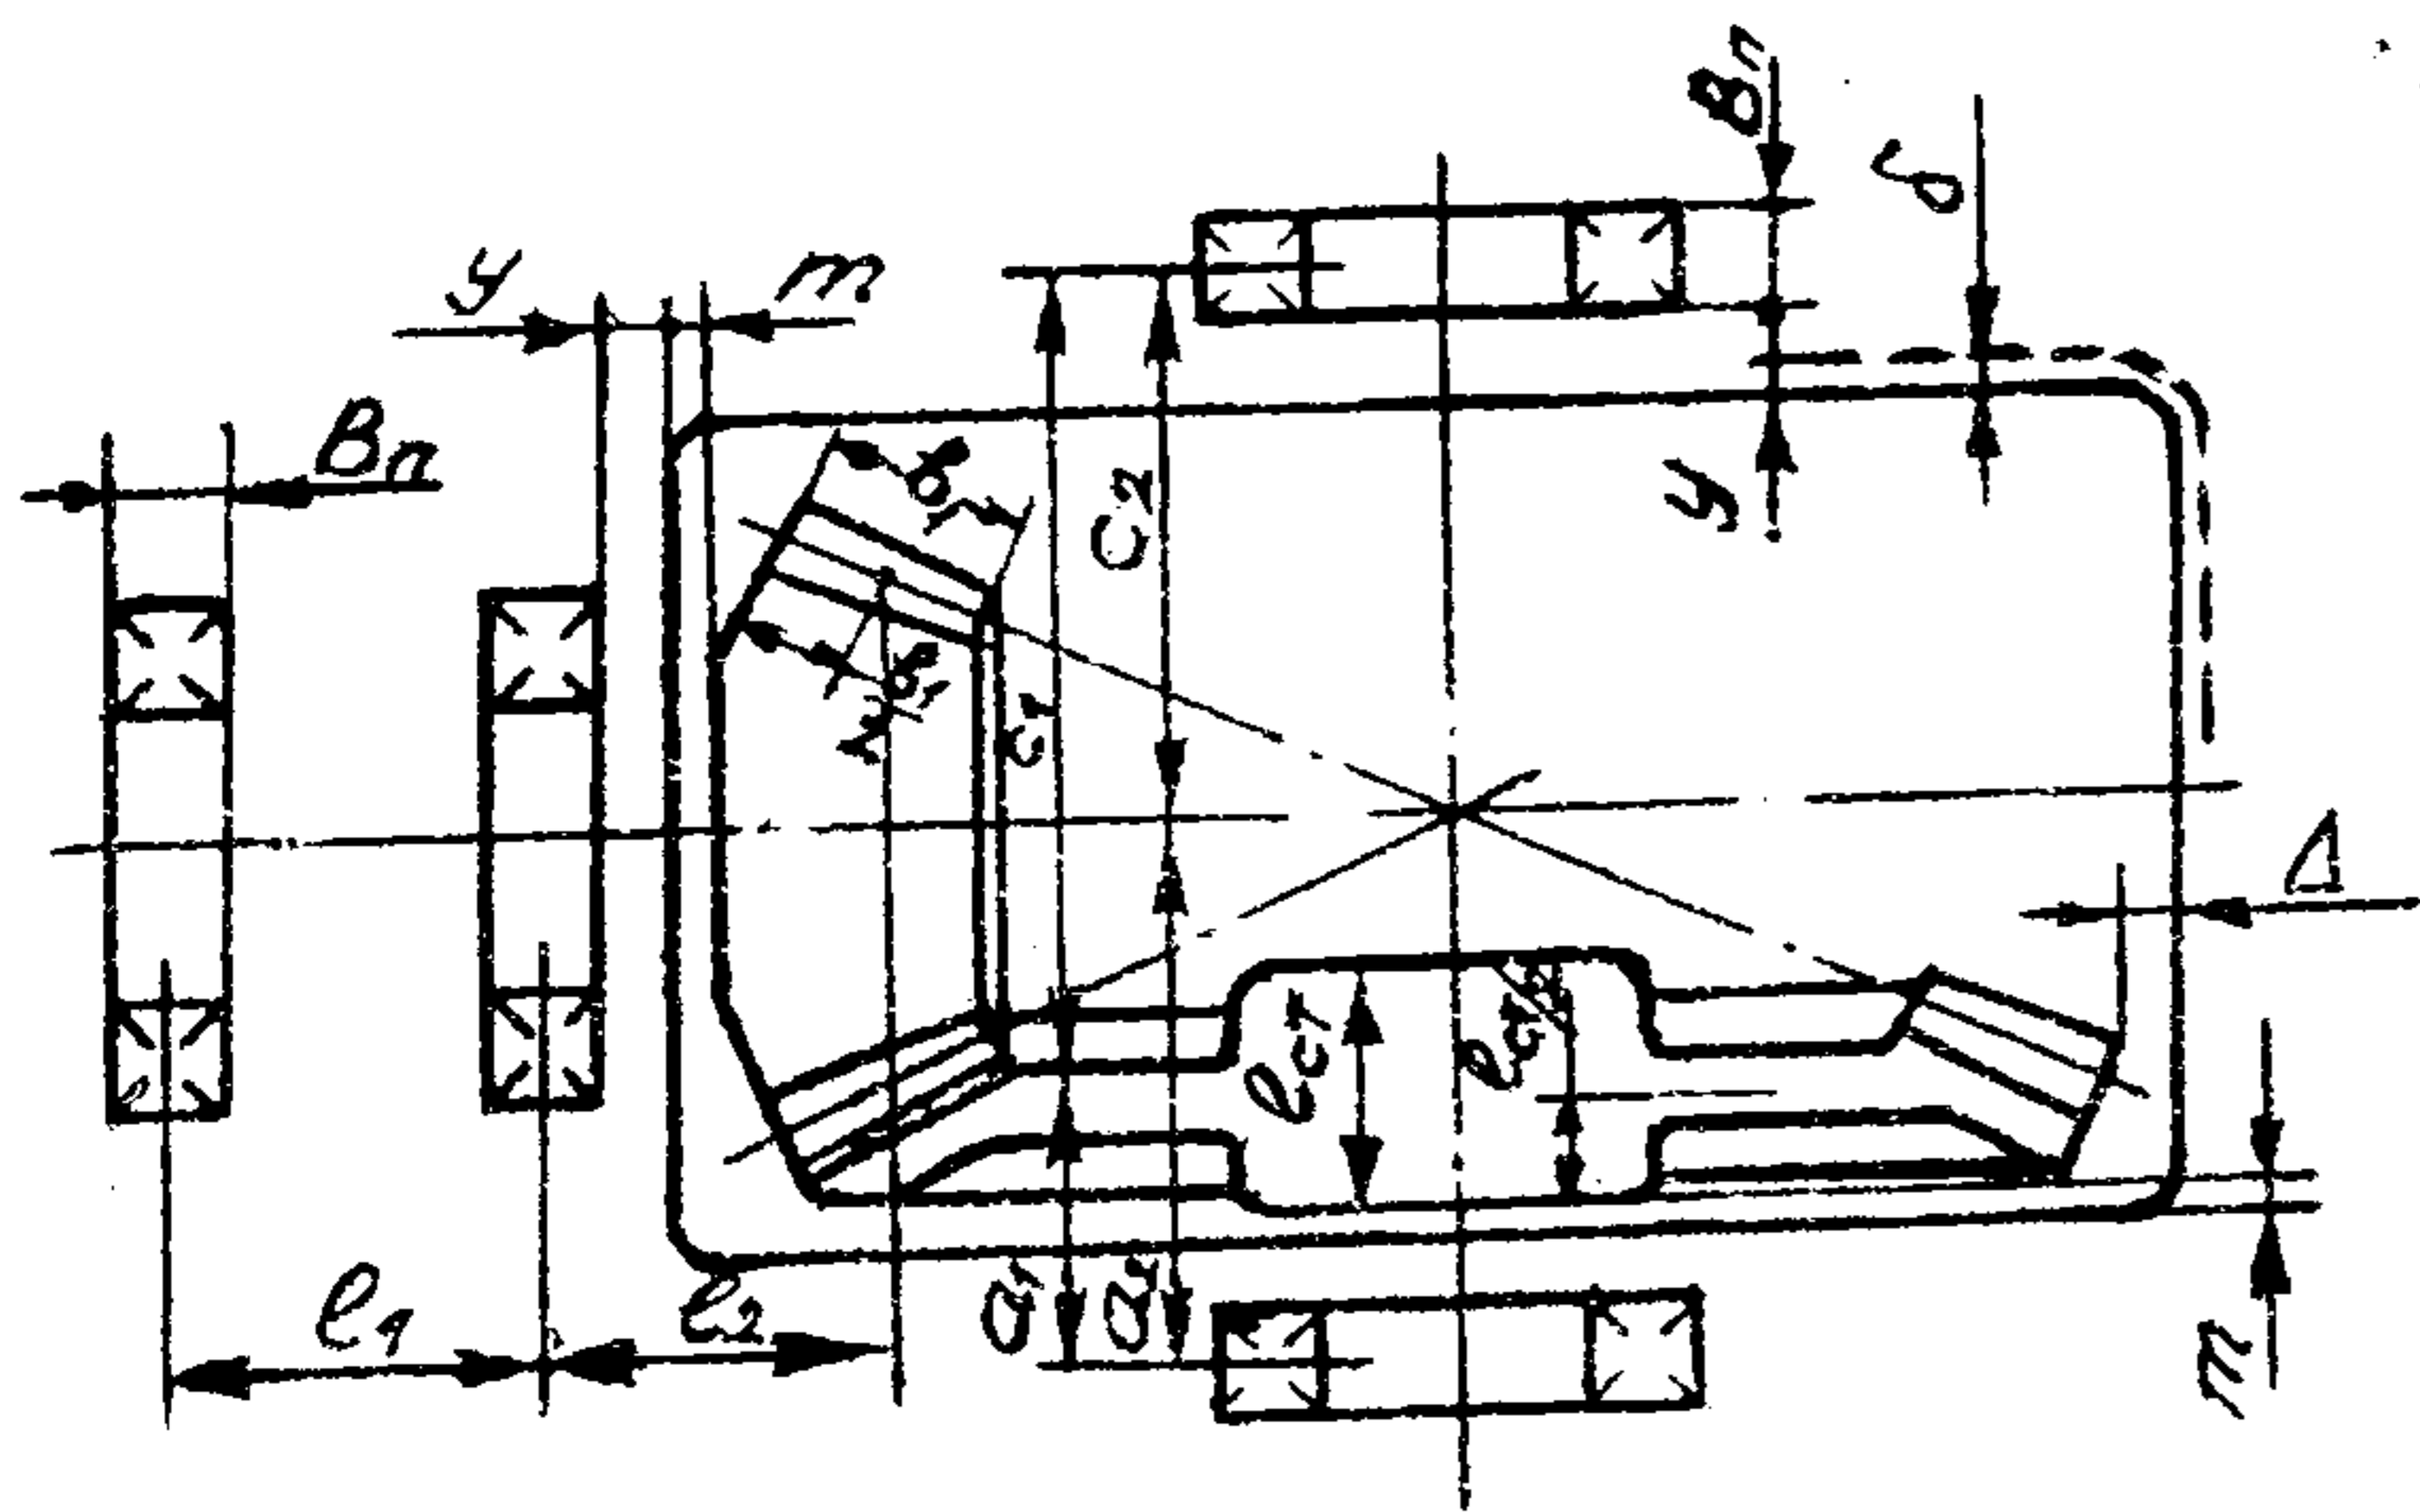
Эскизная компоновка конического зубчатого редуктора
